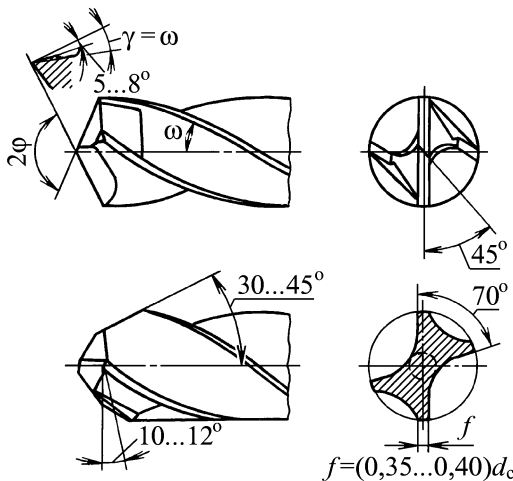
Геометрические параметры четырехкромочного спирального твердосплавного сверла
